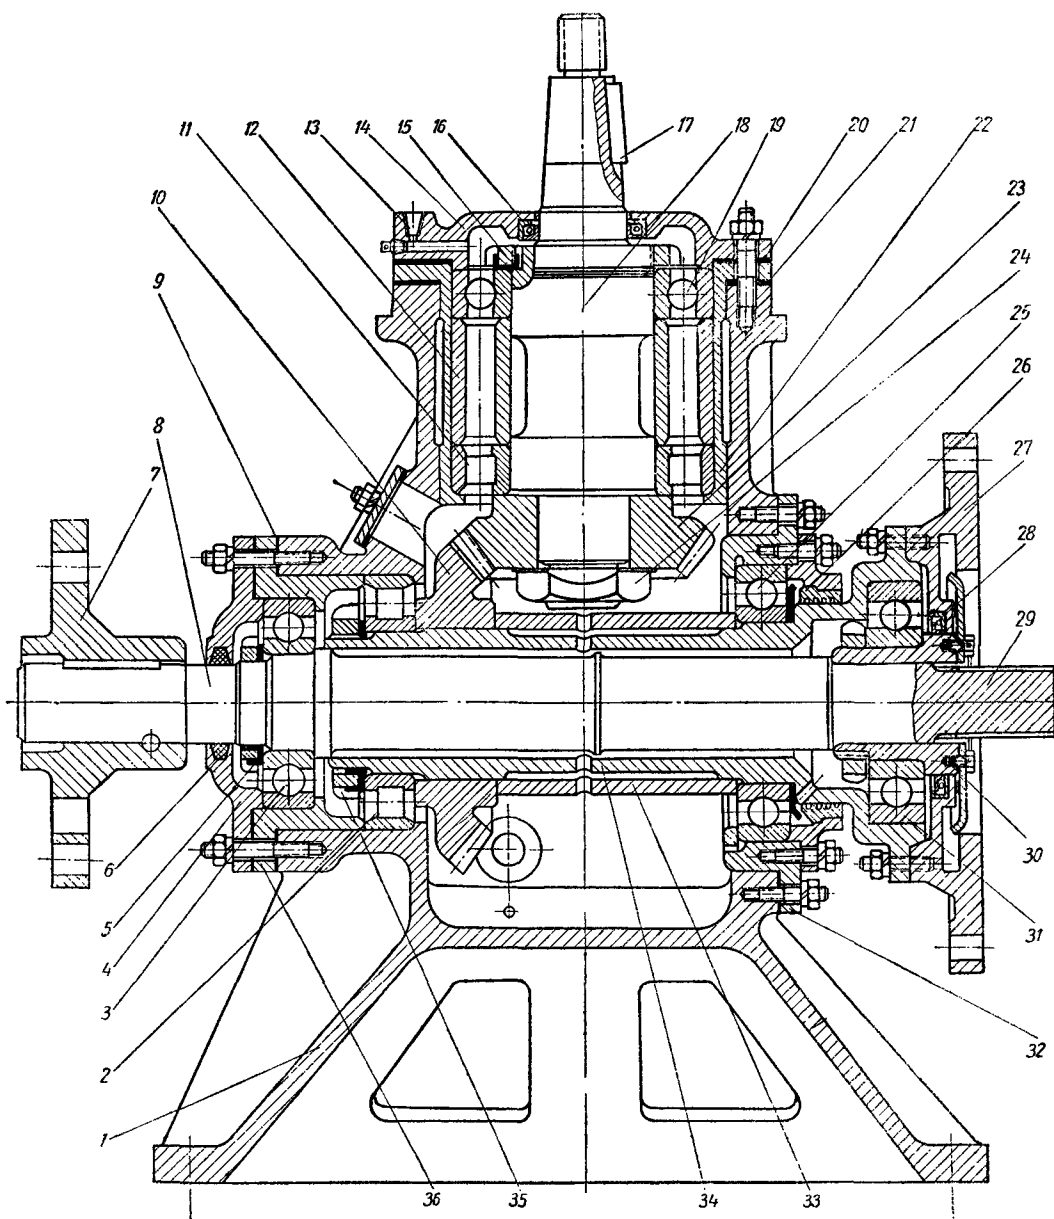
Установка редуктора вентилятора тепловоза ТЭ2.
